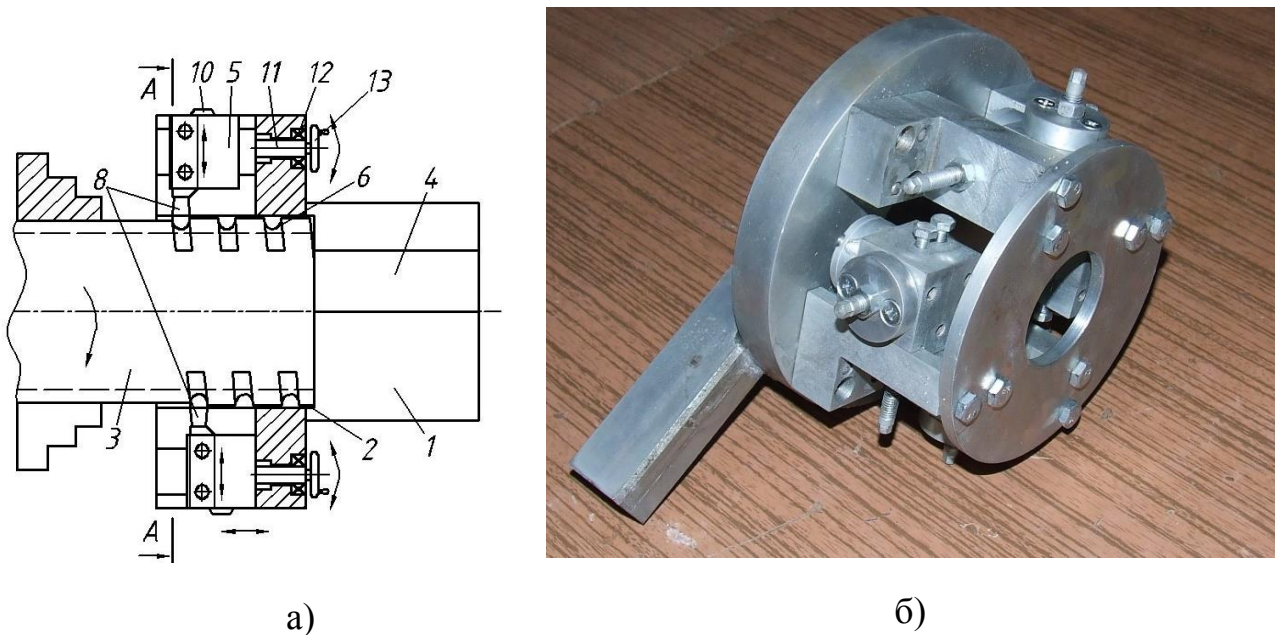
Пристрій для нарізання гвинтової канавки робочого органу екструдера: а) конструктивна схема; б) загальний вигляд
